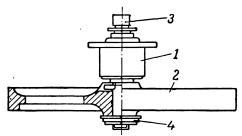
Левый узел. 1 — корпус подшипника; 2 — маховик; 3 — ось; 4 — гайка.
